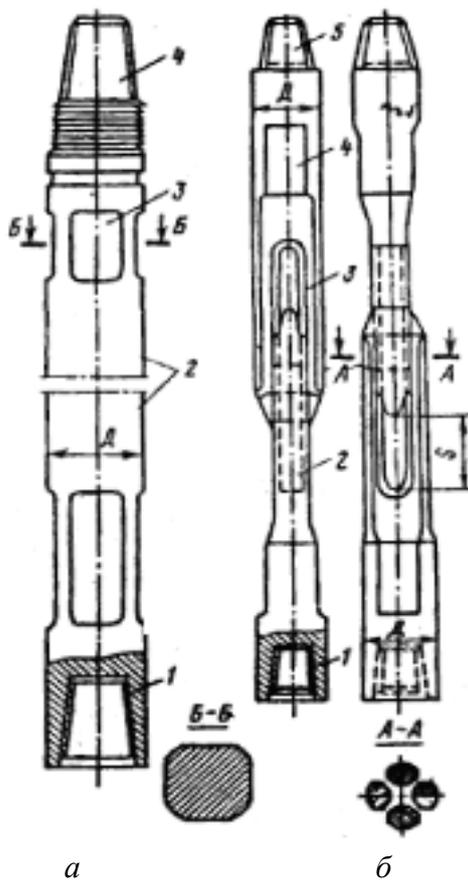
Элементы бурового снаряда: *a* – ударная штанга: 1, 4 – резьбы; 2 – корпус; 3 – лыски; *б* – раздвижная штанга (ножницы): 1, 5 – резьбы; 2, 3 – звенья; 4 – лыски
